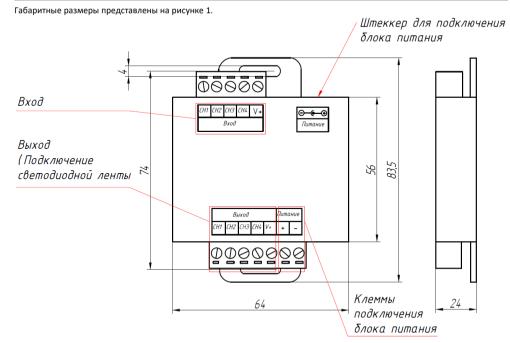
Габаритные размеры Усилитель GA-2 GL-12V288WCH4.
